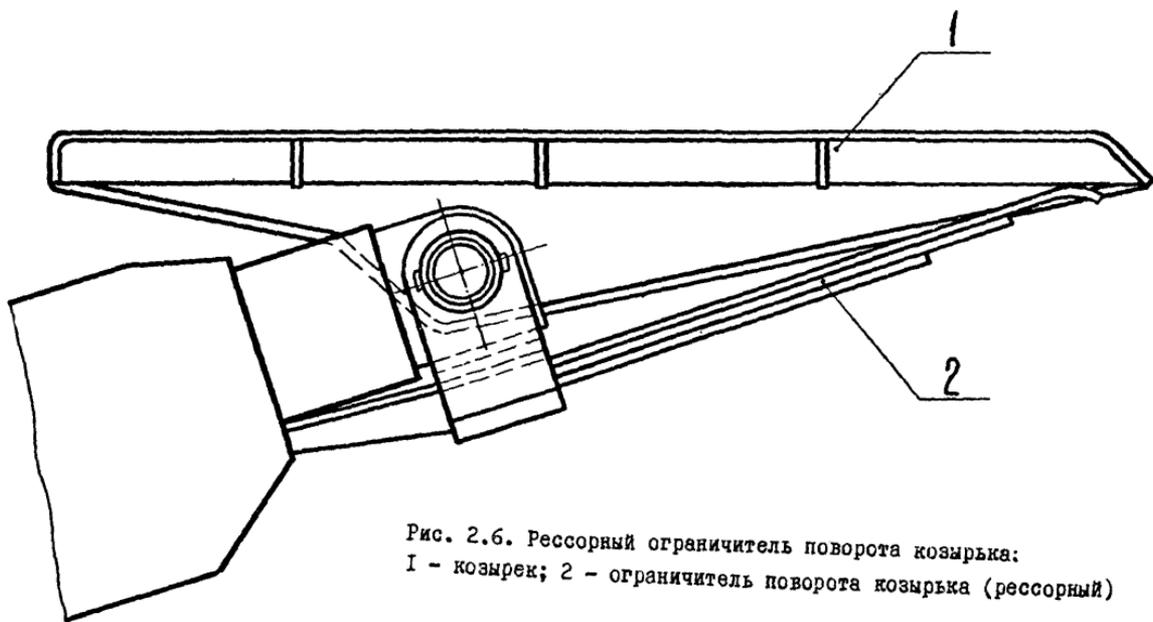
Рессорный ограничитель поворота козырька:
